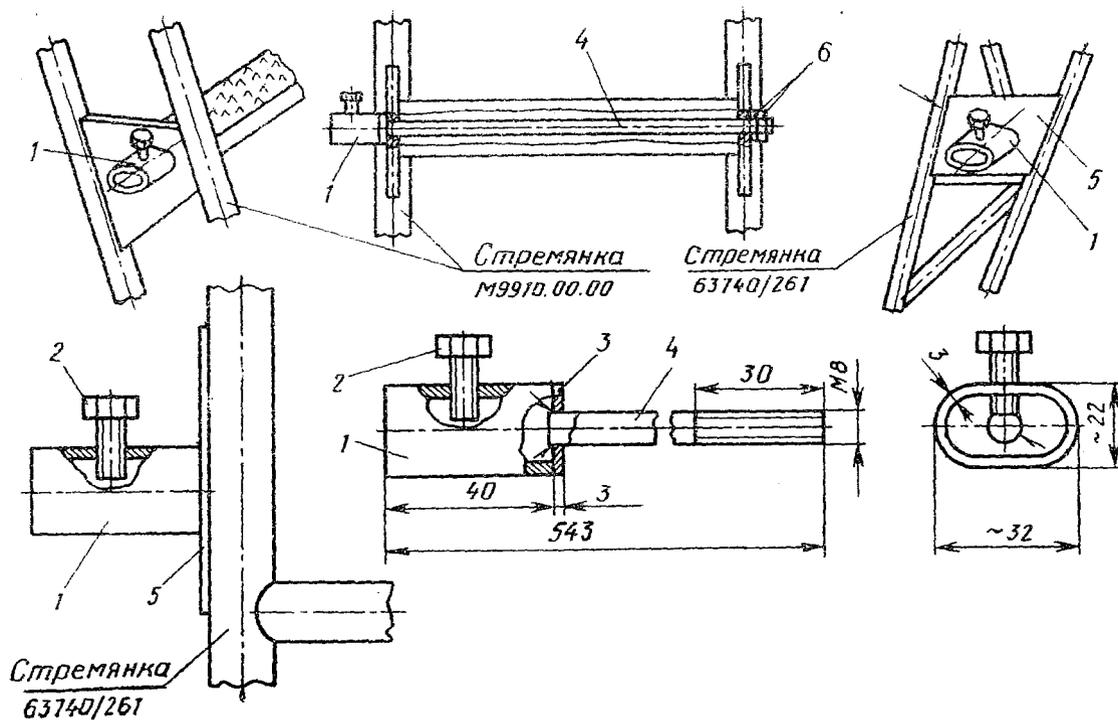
Приспособление для сборки ротора центрифуги ТЦМ-25 и его расположение на стремянках М9910.00.00 и 63740/261:
